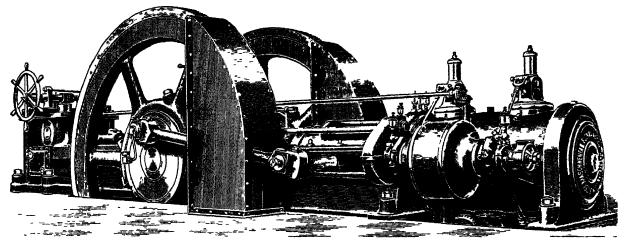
Moderne Brikettpresse mit Ventilsteuerung der MASCHINENFABRIK BUCKAU A -G zu Magdeburg.
